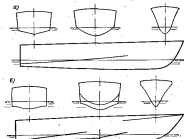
Комбинированные обводы корпусов: а — вербовидный; б — реечный.
